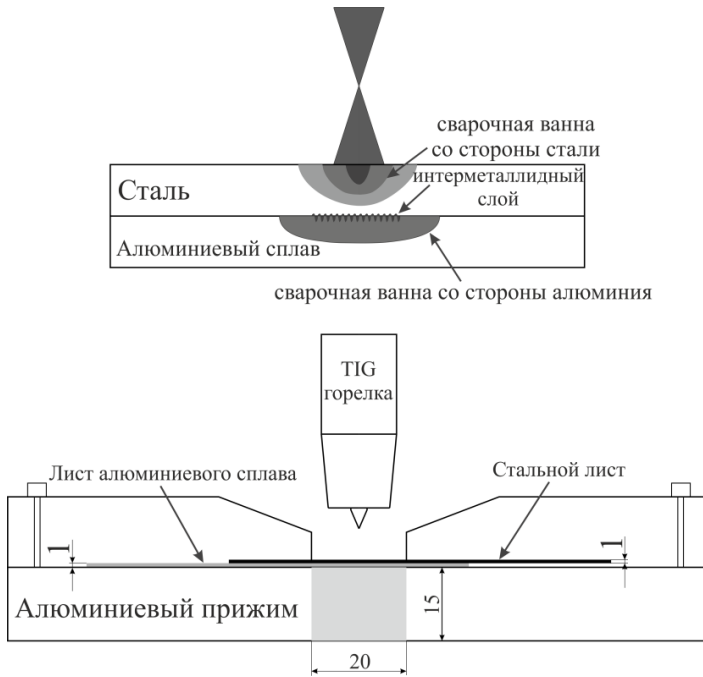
Схема TIG сварки нахлесточного соединения стали с алюминием без присадочной проволоки [13]
